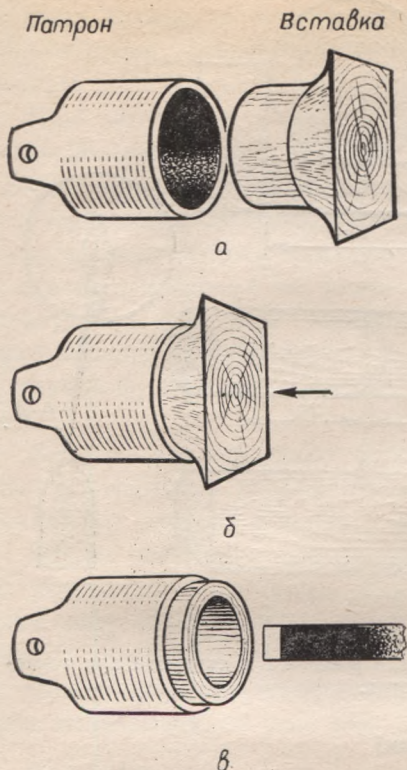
Закрепление в патроне вставки из твердой древесины:
